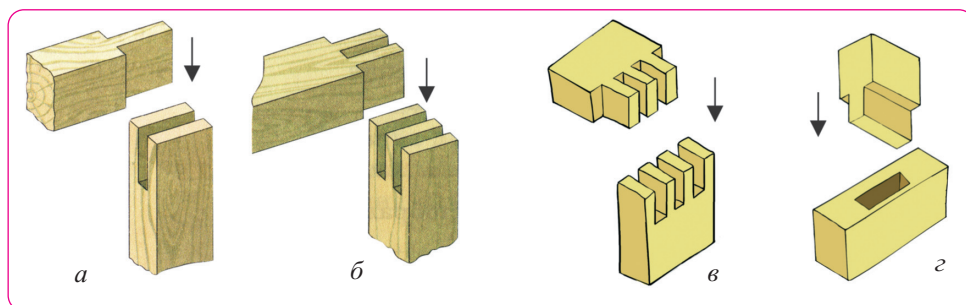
Виды шиповых соединений: а – открытое одинарное, б – открытое двойное; в – открытое тройное; г – прямое закрытое
